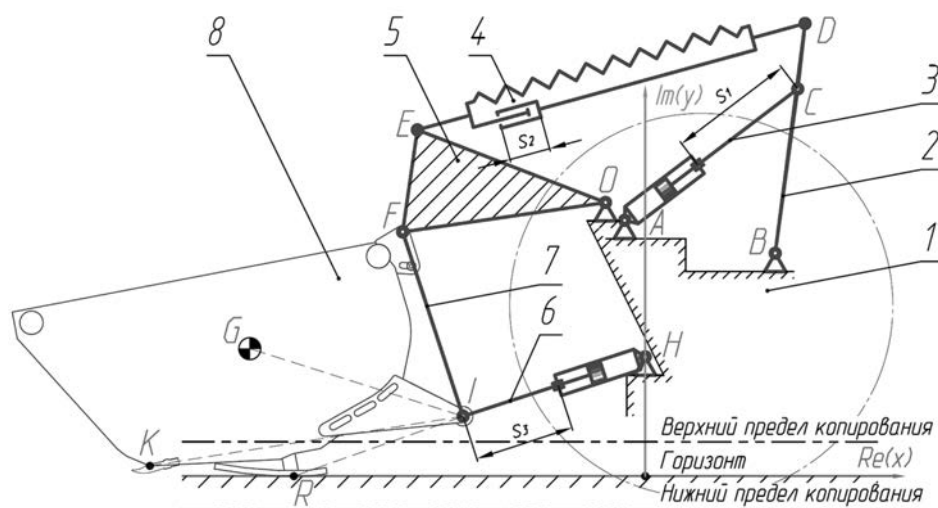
Кинематическая схема механизма агрегатирования: 1 – рама; 2, 5 – двуплечий поворотный рычаг; 3 – гидроцилиндр подъема; 4 – блок уравнивающих пружин с телескопической тягой; 6 – гидроцилиндр угла атаки нижней тяги; 7 – растяжка; 8 – адаптер
